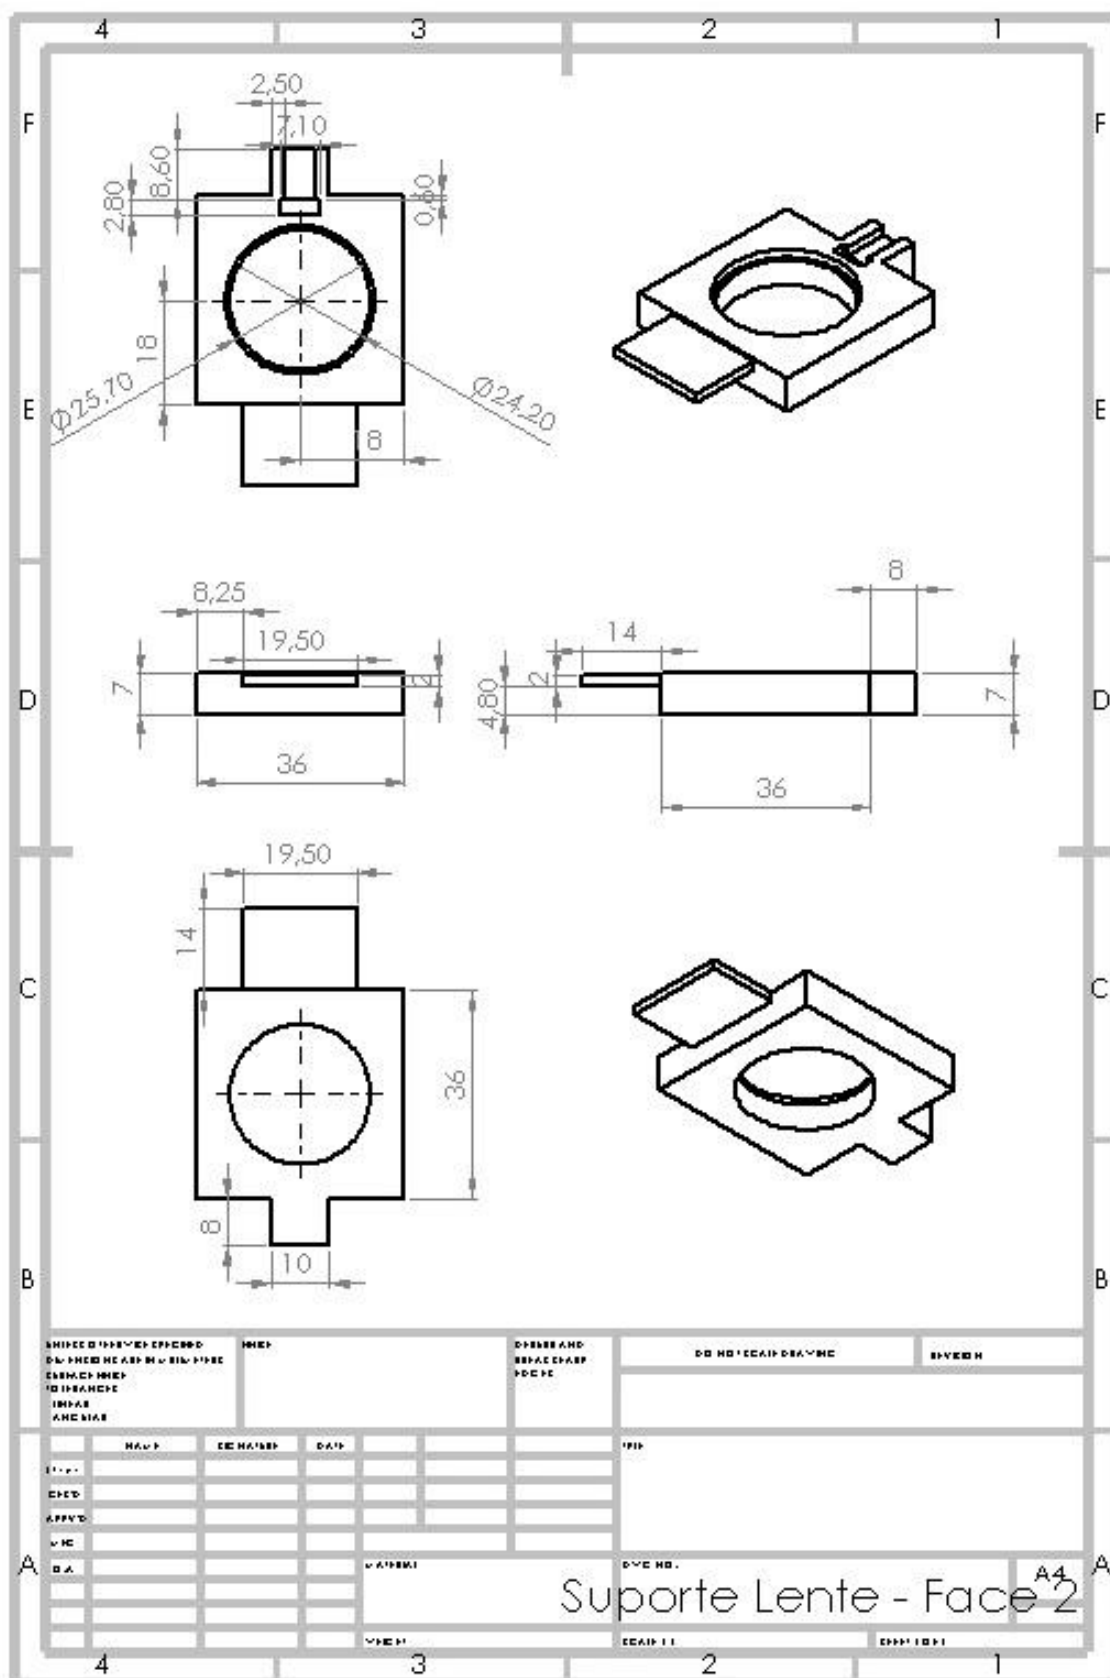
Desenho técnico da peça Suporte Lente - Face 2
